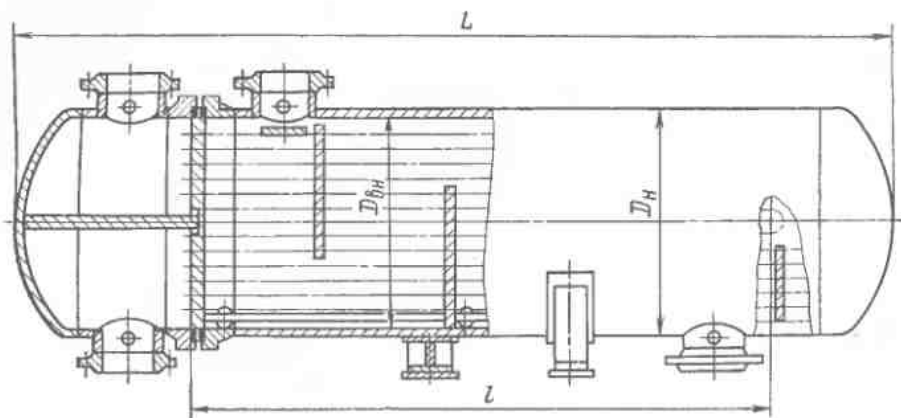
Кожухотрубчатый двухходовой теплообменник с U-образными трубами
